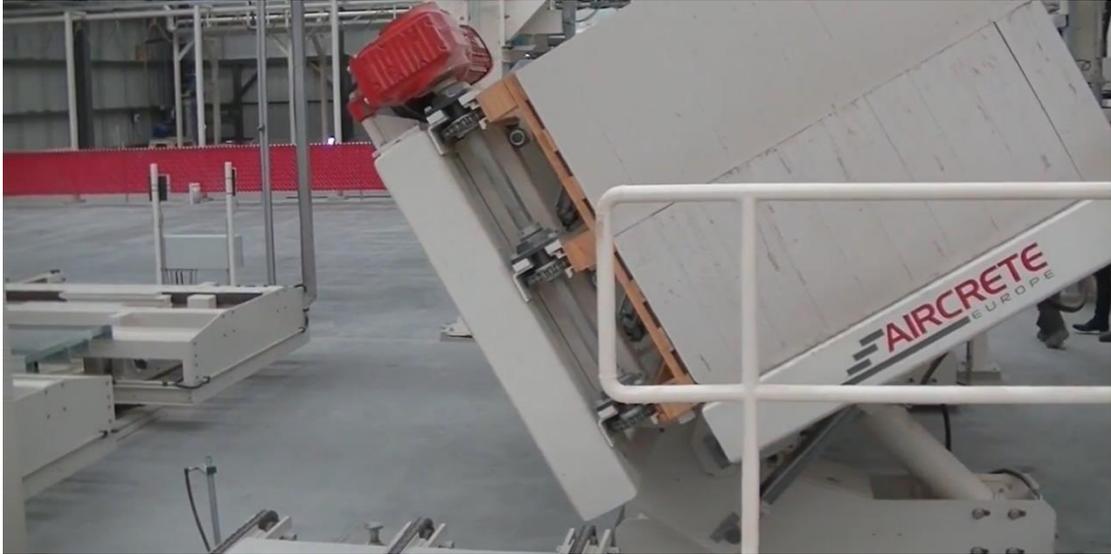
Fotografía de la planta de prefabricados de concreto celular/ Imagen de AIRCRET SMKT
